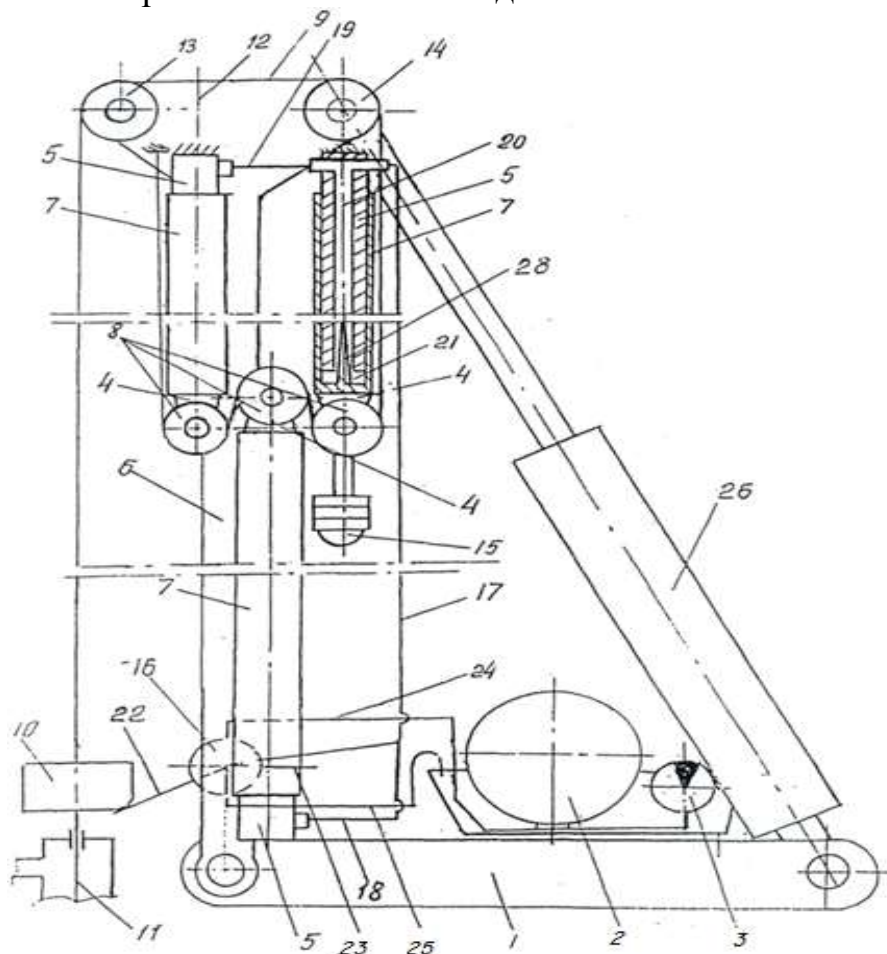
Качалка с вертикальным расположением гидроцилиндров
